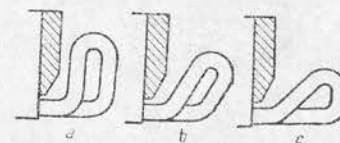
Forma capetelor de bobină la bobinajul în coroană.
